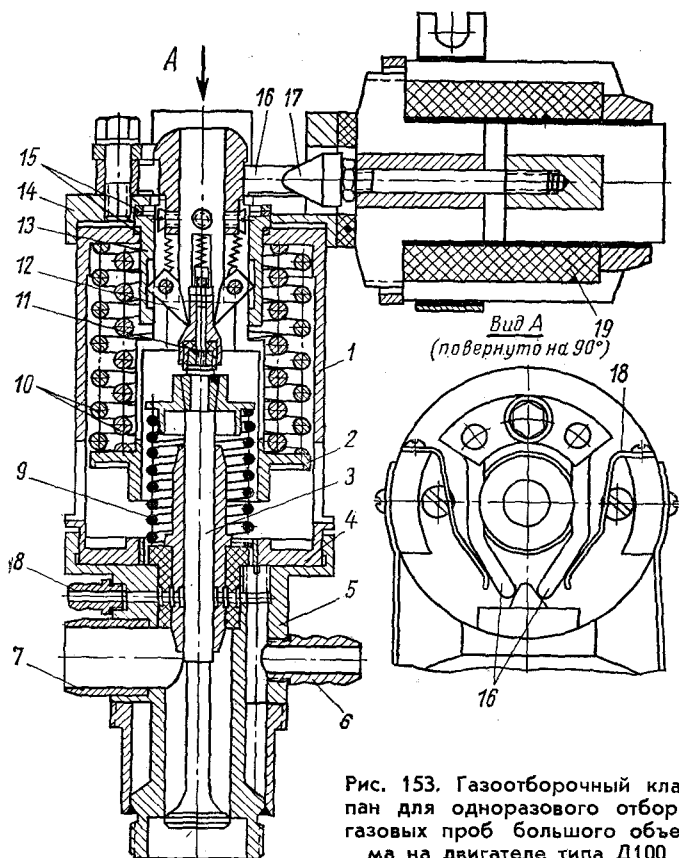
Газоотборочный клапан для одноразового отбора газовых проб большого объема на двигателе типа Д100
